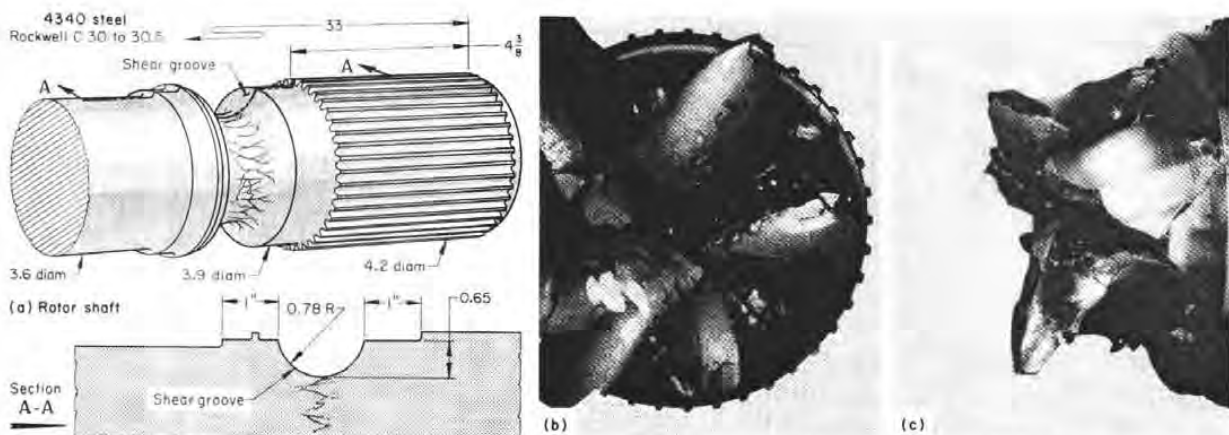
Flecha de acero 4340 de un rotor que falló por fatiga a torsión
